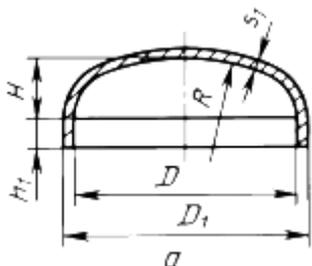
Основные размеры эллиптической крышки [2]
